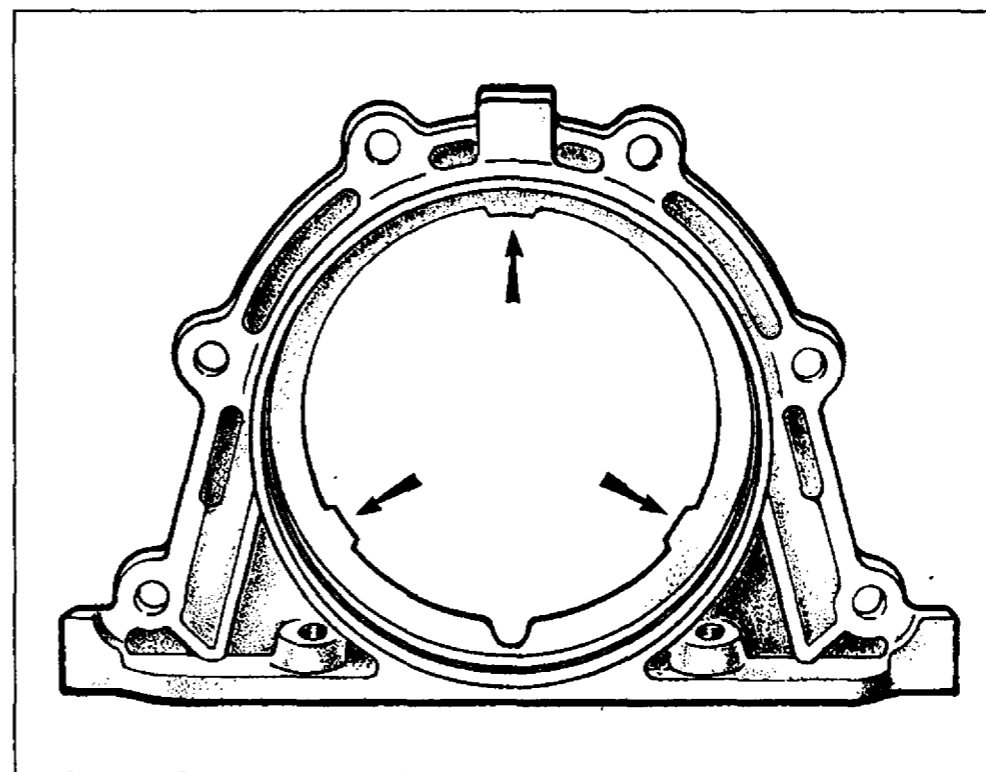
Держатель заднего сальника коленчатого вала. Стрелками показаны выступы для центрирования держателя относительно фланца коленчатого вала
